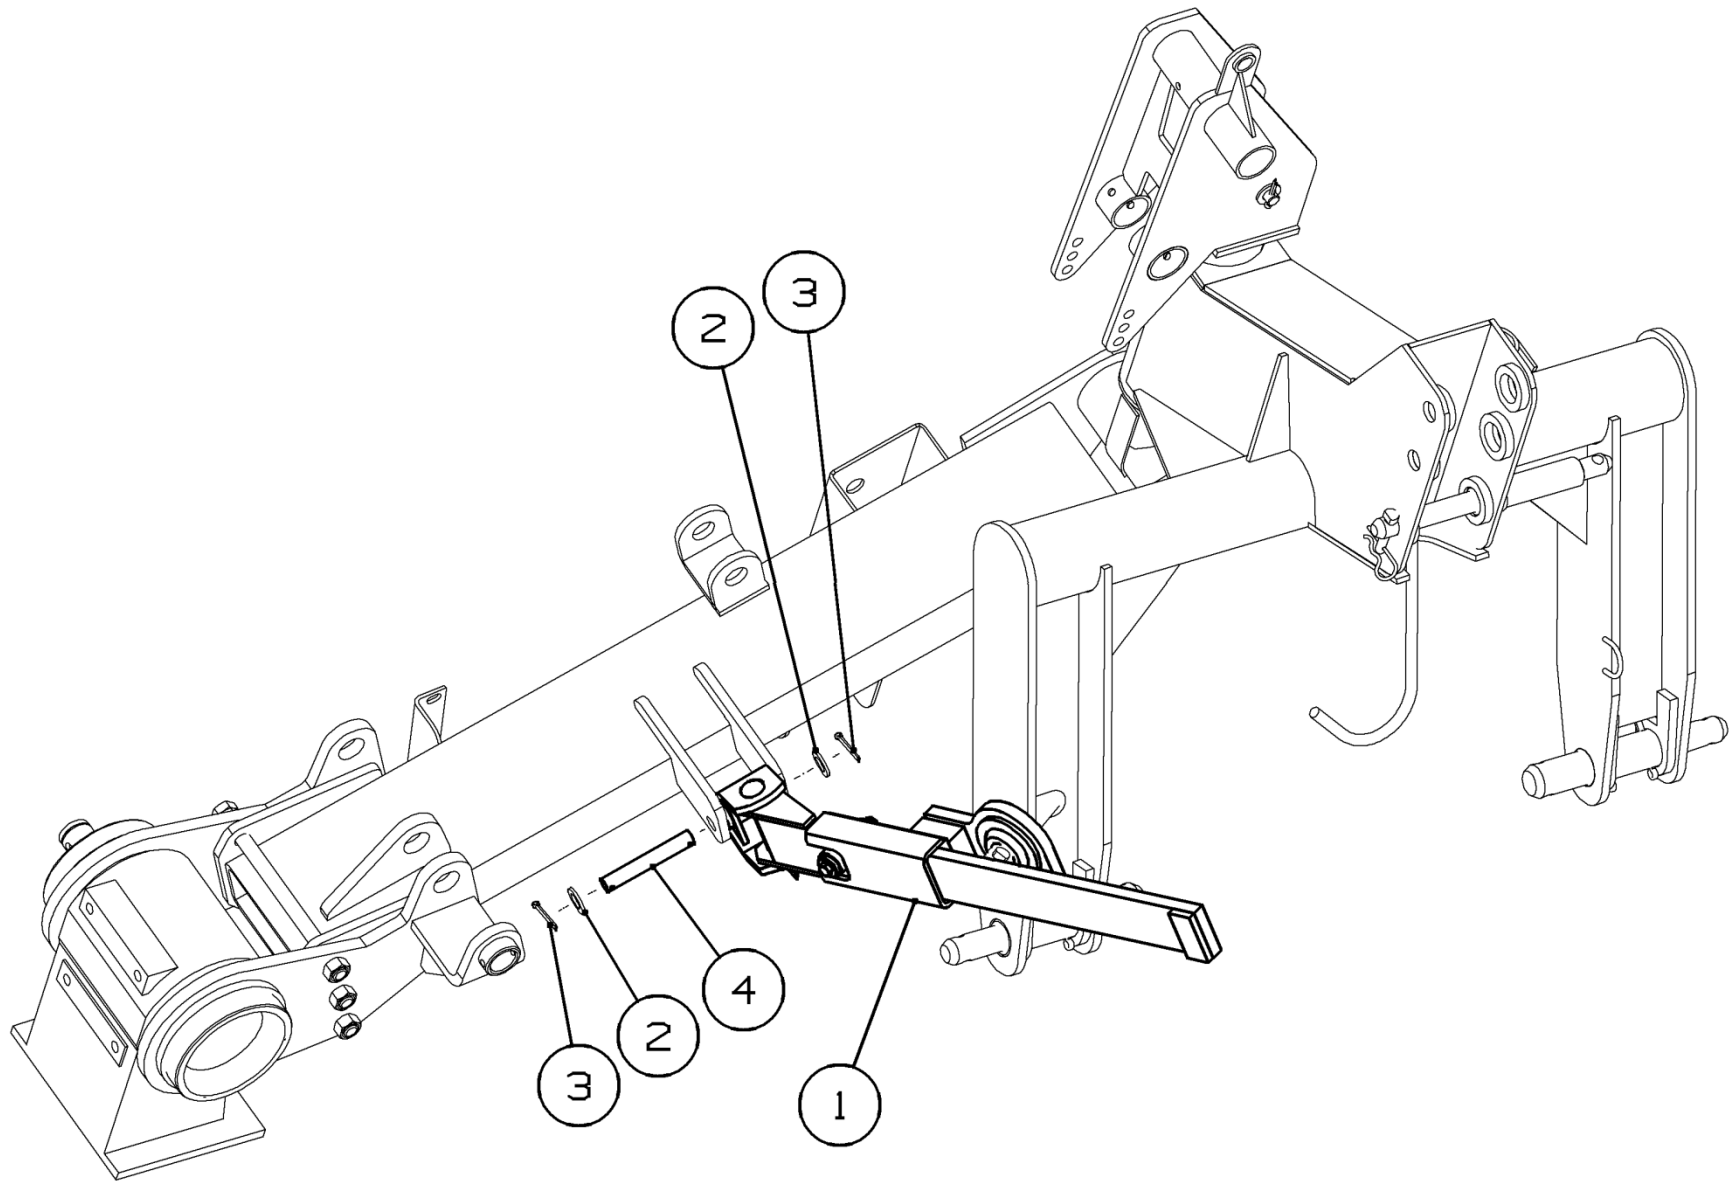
КРК-2.4.06.000 Установка предохранителя
